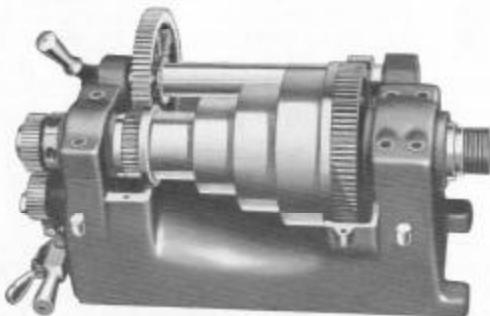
Cabeçote de engrenagens redutoras, sem guarda-engrenagens.
